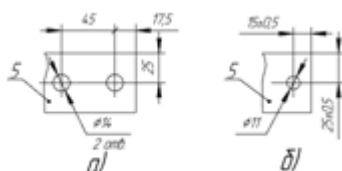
Контактный вывод разъединителя со стороны неподвижной колонки
